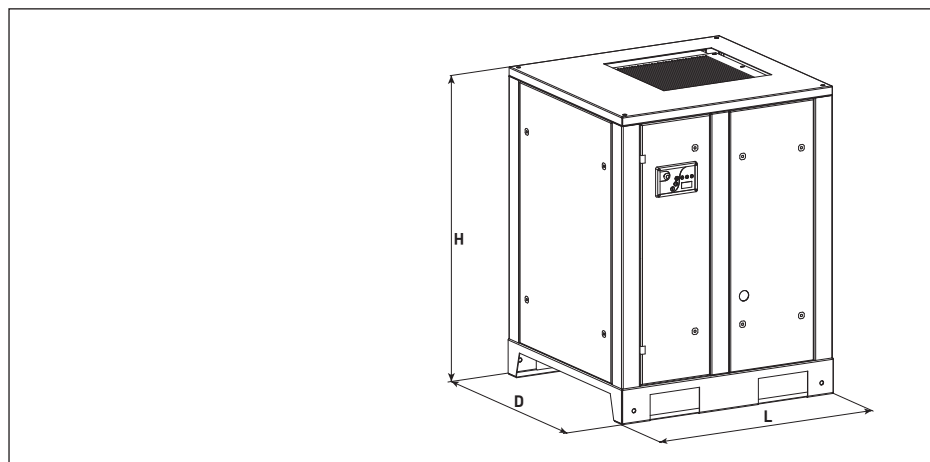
Размеры компрессора A07.. – A22.
